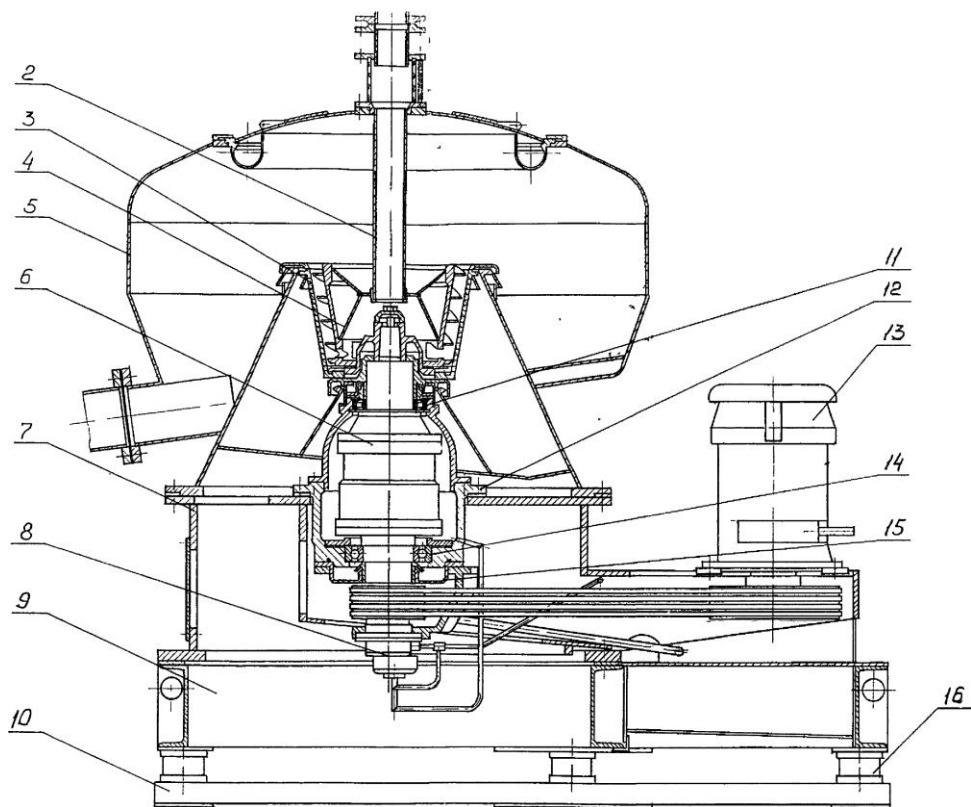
Центрифуга ОГШ-631К-06 (розріз).
